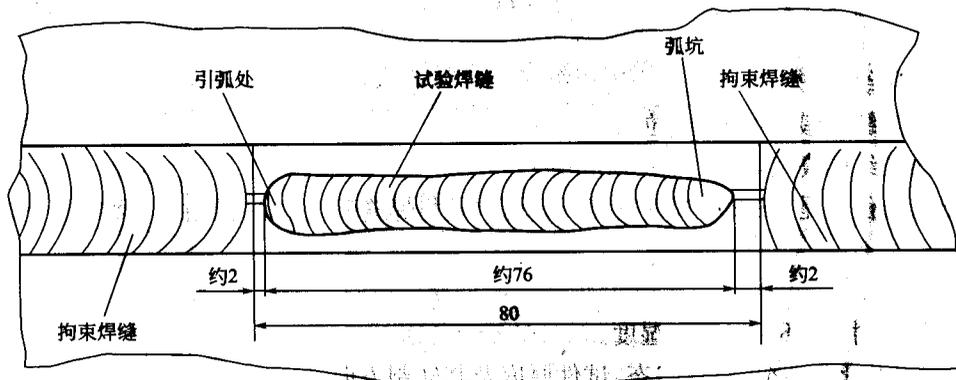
采用焊条自动送进装置焊接试验焊缝位置
